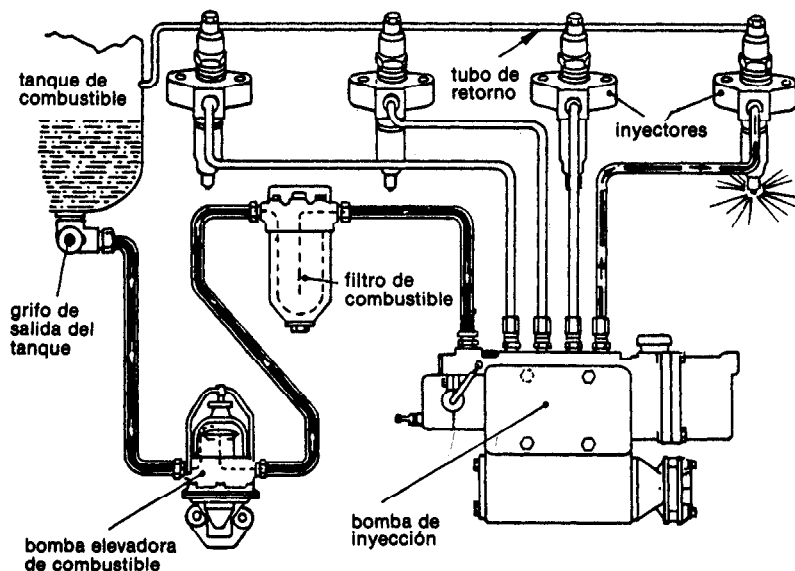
Sistema básico de combustible con bomba de inyección en línea
